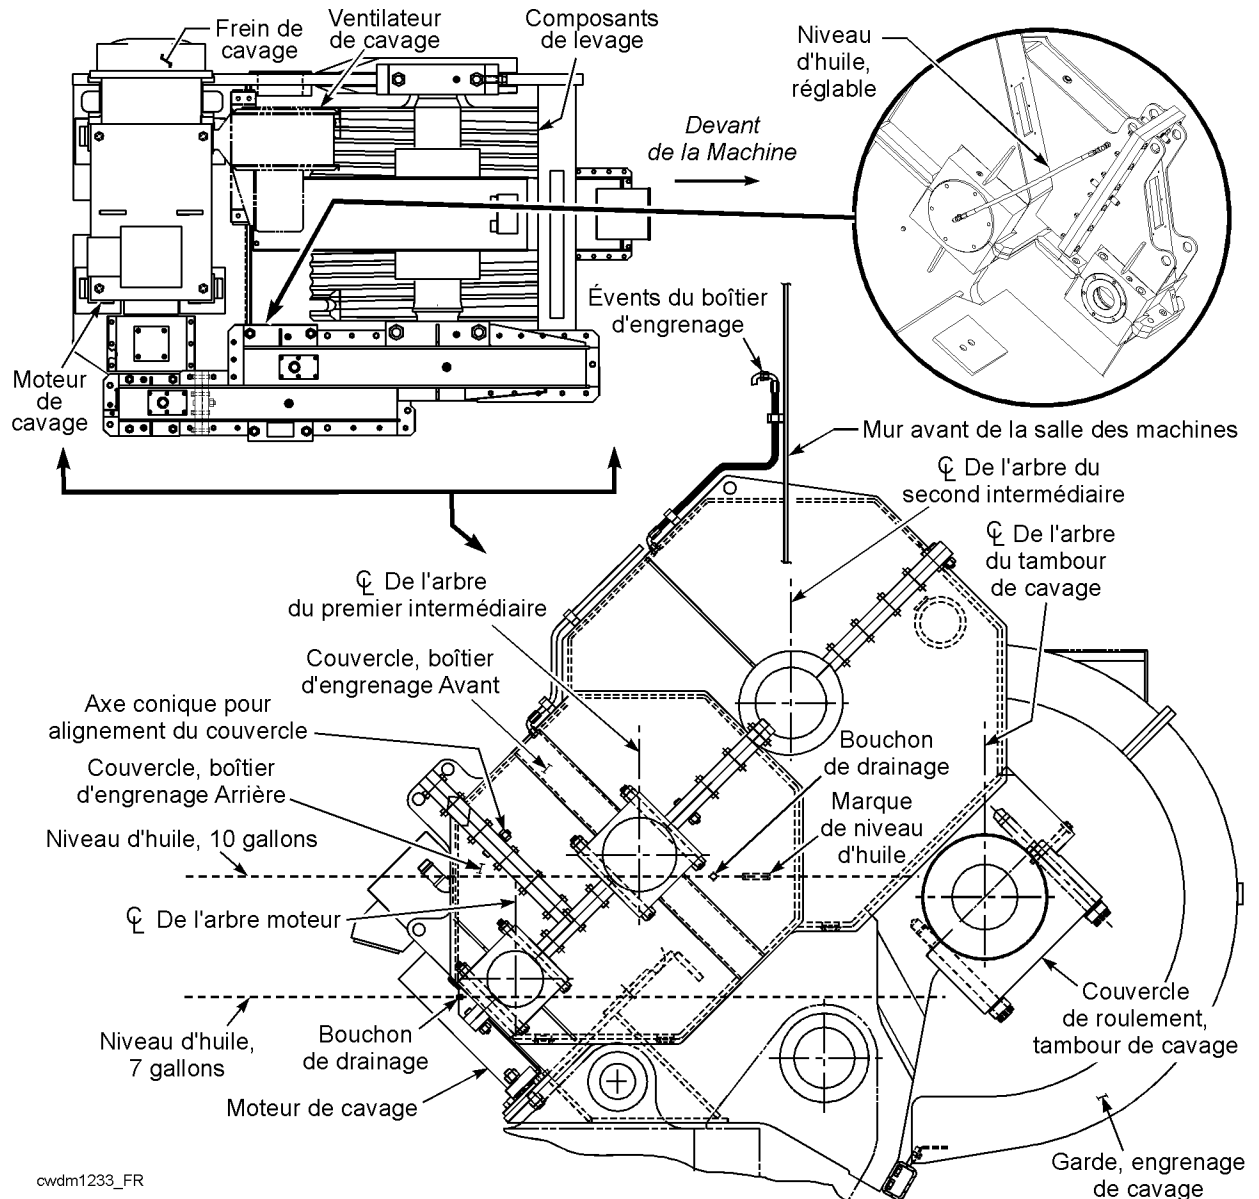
Boîtier d'engrenage de levage - Coupe transversale
